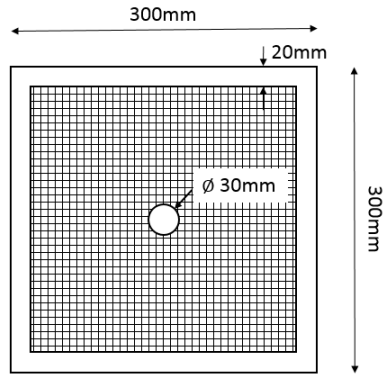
Desenho esquemático da placa GFRP utilizada.
